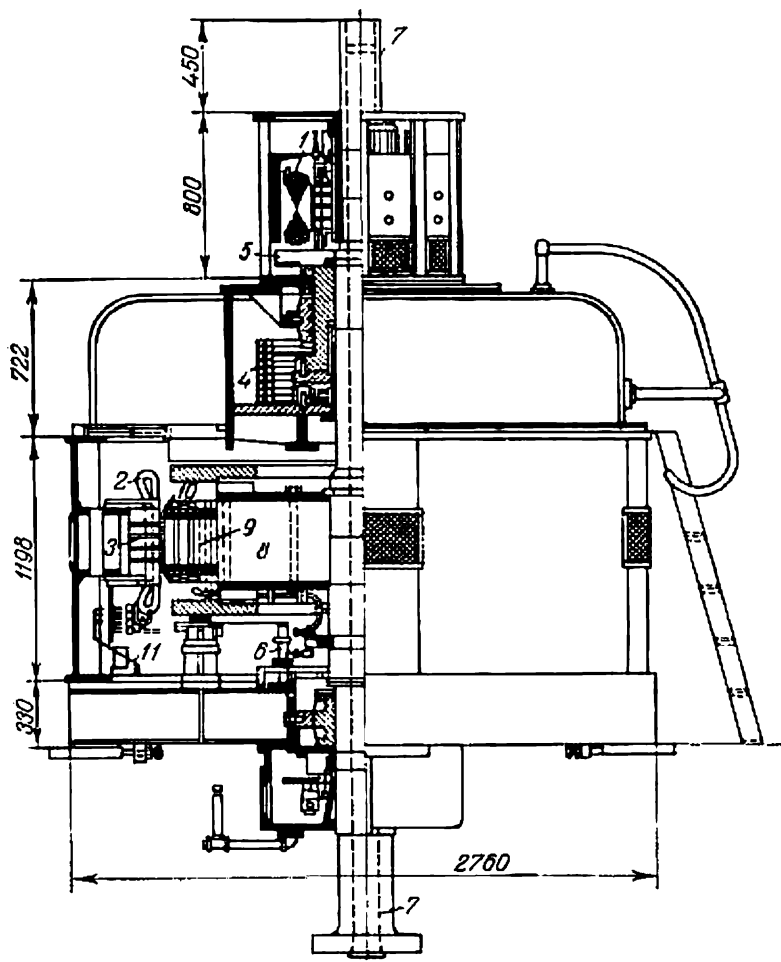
Coupe longitudinale d'un alternateur hydraulique suspendu :
